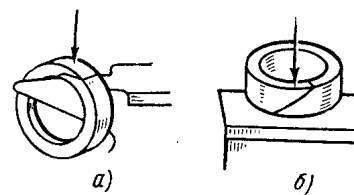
Схема кузнечной сварки колец из полосового материала:
